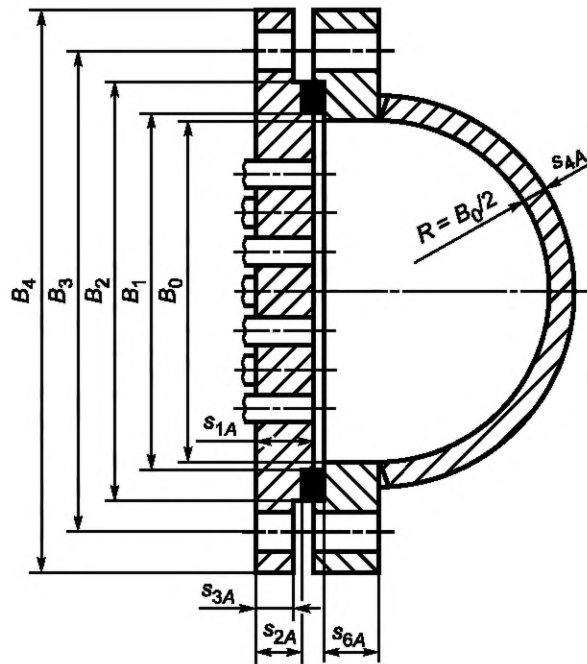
Камера разъемной конструкции со сварной полуцилиндрической крышкой
